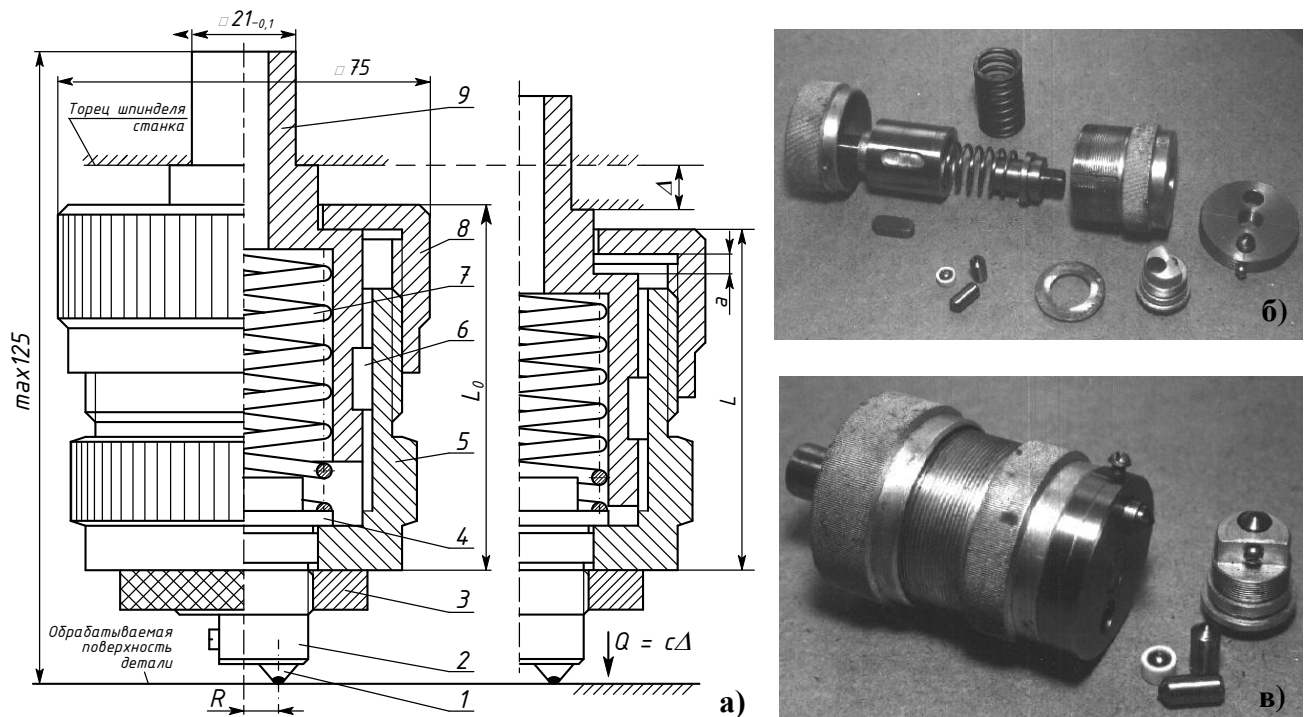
Конструкция инструмента для алмазного выглаживания плоских поверхностей деталей: а – конструкция выглаживателя: 1 – вставка с индентором из АСПК; 2 – держатель; 3 – гайка; 4 – корпус держателя; 5 – корпус; 6 – шпонка; 7 – пружина; 8 – крышка; 9 – хвостовик; б – выглаживатель в разобранном состоянии; в – общий вид алмазного выглаживателя с различными держателями и инденторами
